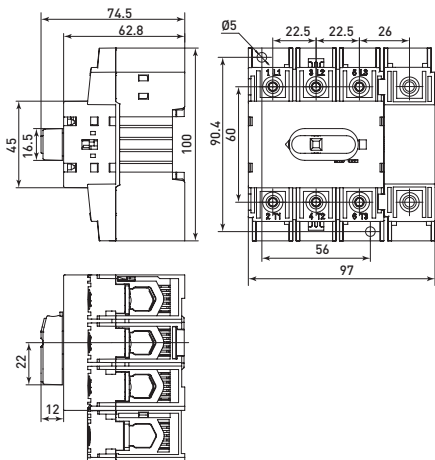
Габаритные и установочные размеры рубильников 63-125А 4Р
